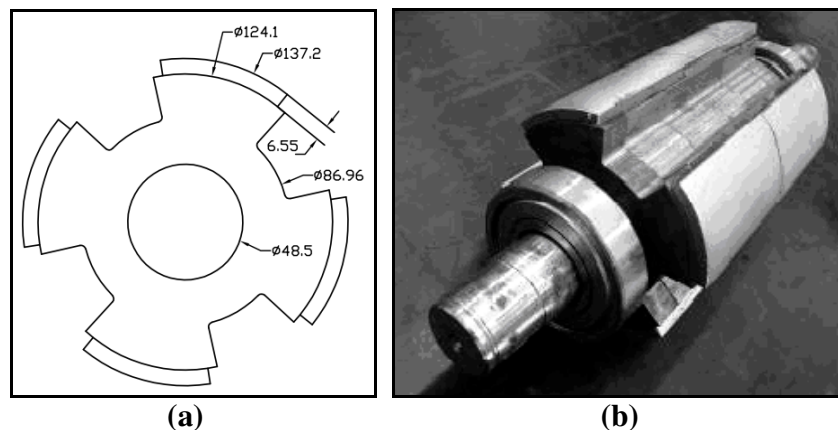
Rotor de polos salientes – (a) Desenho esquemático – (b) rotor montado [30]
